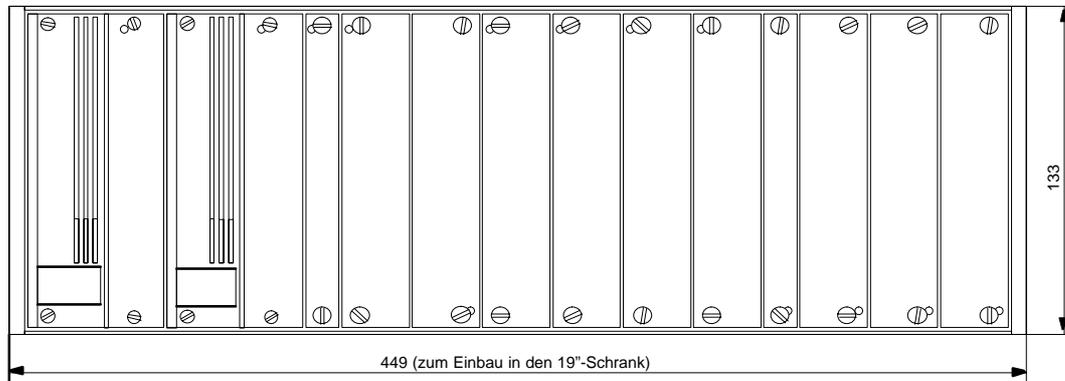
Aktiver Sternkoppler ASGE (Frontansicht; Maße in mm)
